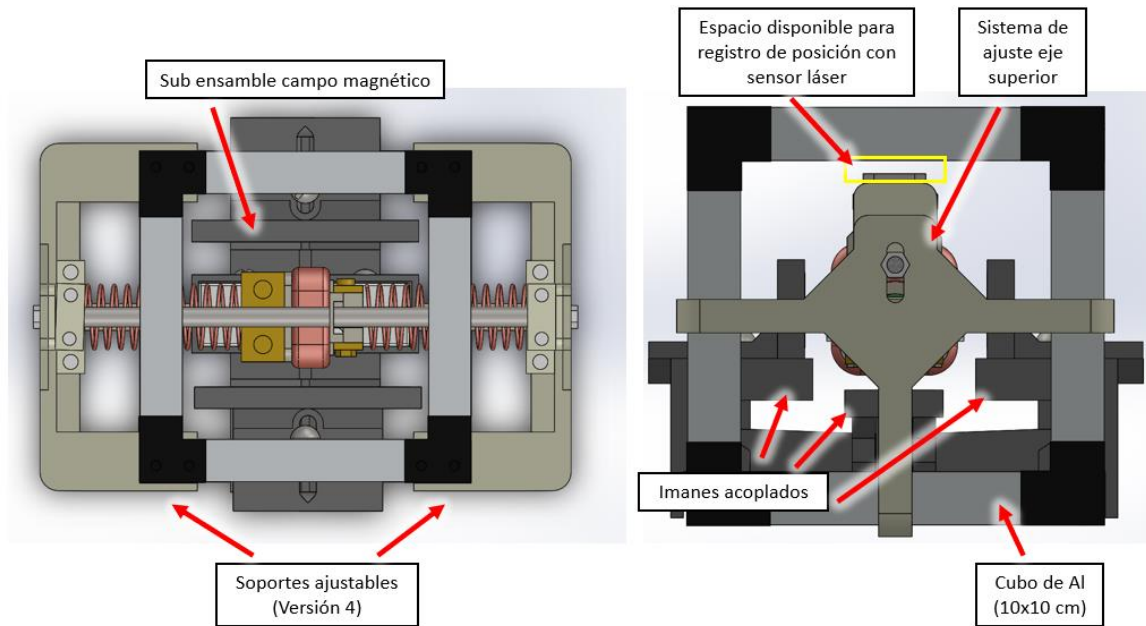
Amortiguador electromagnético ensamblado. (A) Vista Superior; (B) Vista frontal
